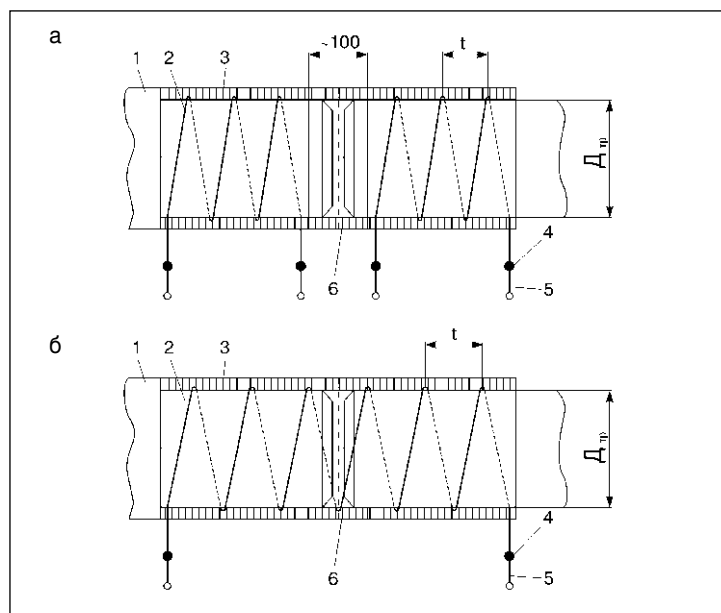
Схемы установки электронагревателей КЭН для подогрева при сварке кромок труб без стационарной антикоррозионной изоляции: а — при установке КЭН на каждую трубу; б — при установке одного КЭН на свариваемый стык (1 — труба; 2 — секция КЭН; 3 — теплоизоляция на КЭН; 4 — контактное соединение; 5 — токоподводящий кабель; 6 — теплоизоляция на подогреваемых кромках труб); t — шаг витков КЭН; $D_{тр}$ — диаметр трубы
